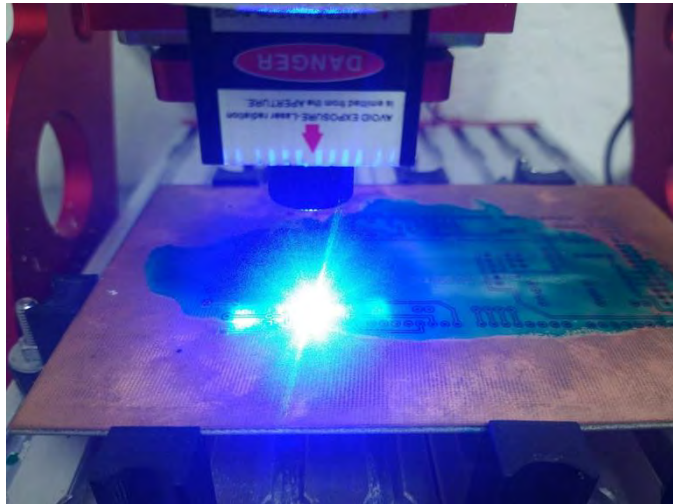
Corte laser del proceso de mascara de soldar doble cara
